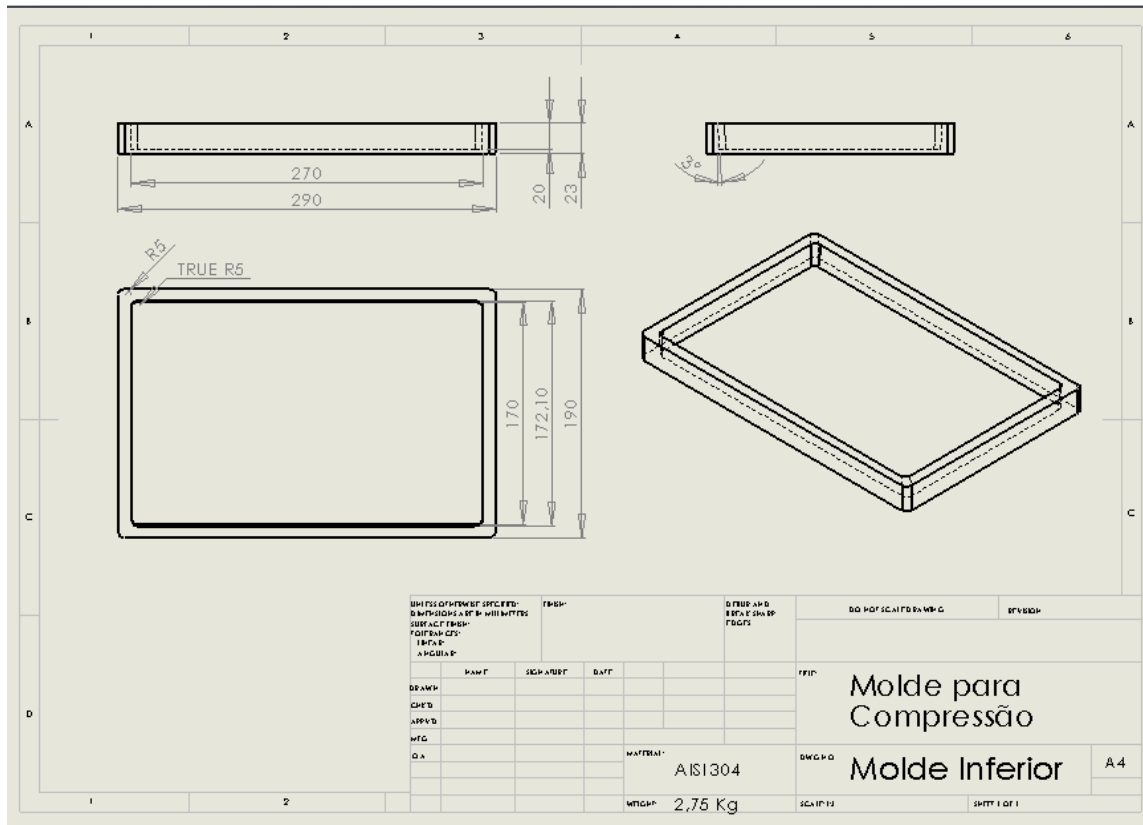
Desenho da parte inferior do molde construído - Molde 2.
